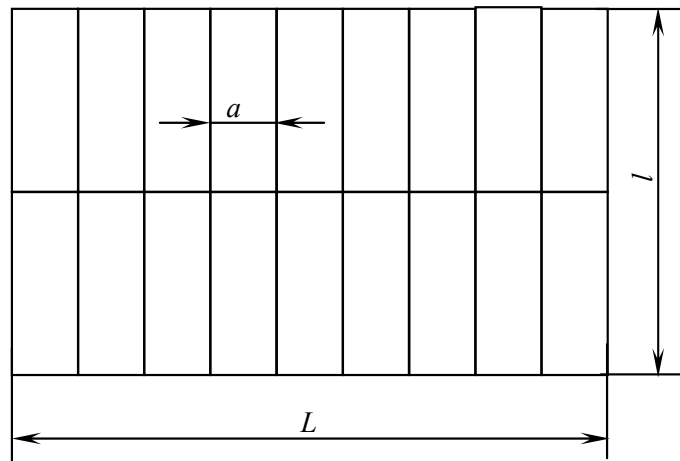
Схема днищового перекриття з розмірами для розрахунку
